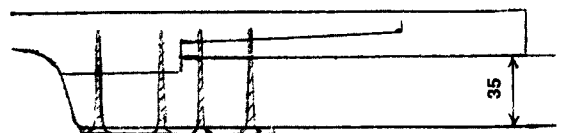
Соединение грифа с корпусом. Шурупы пропущены через стальную пластину
